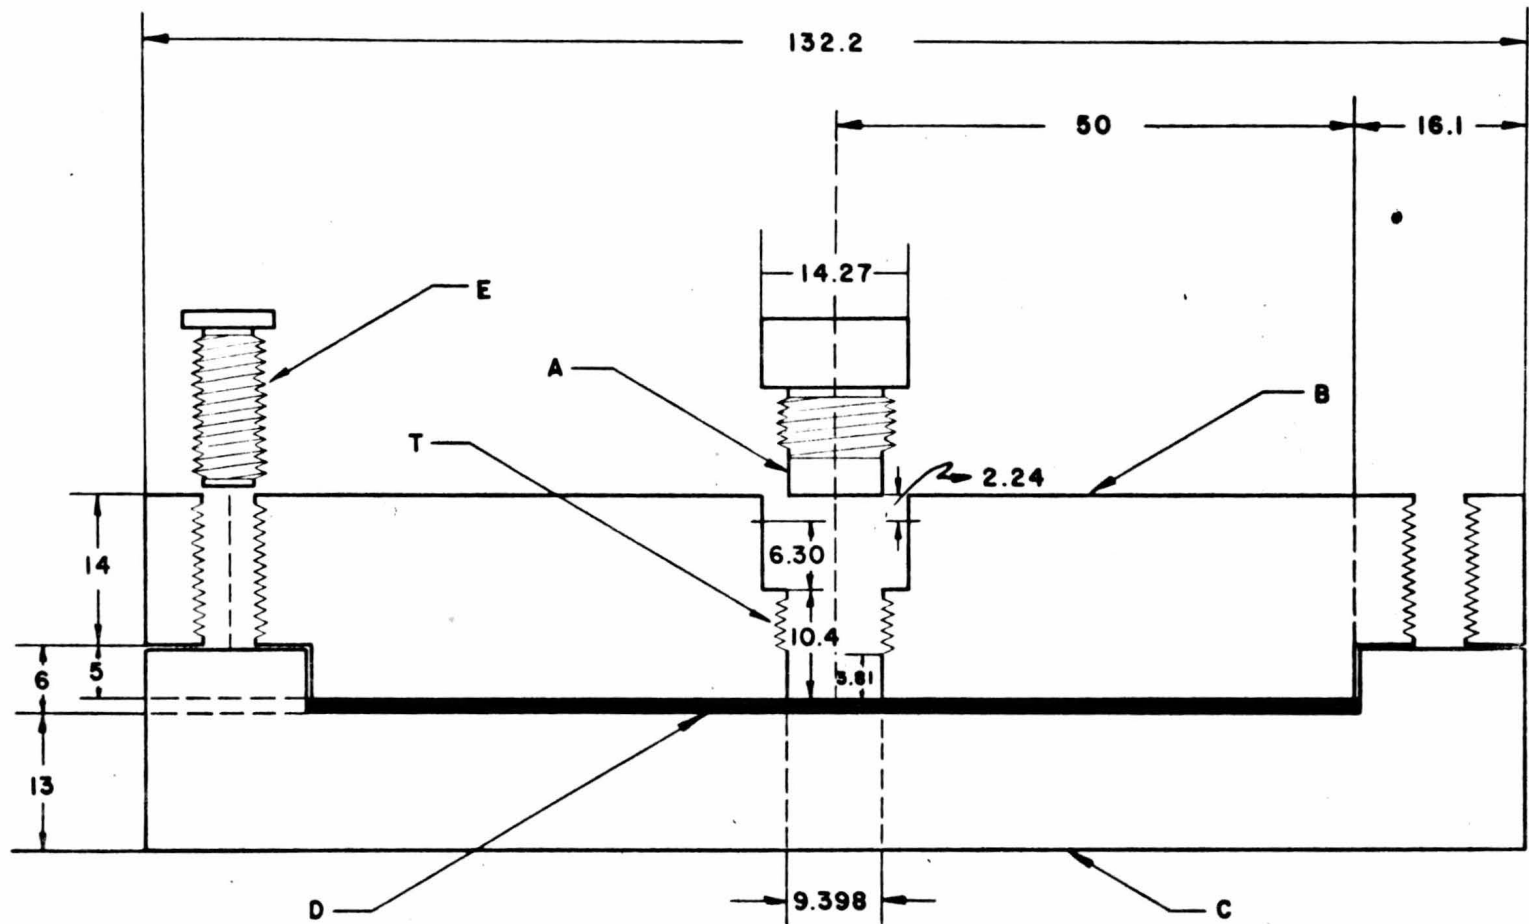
Diseño y Dimensiones (en mm.) del Molde. (A) Transductor de Presión, (B) Molde Macho, (C) Molde Hembra, (D) Cavidad para muestra, (E) Tornillos Allen, (T) Cuerda para fijar Transductor.
